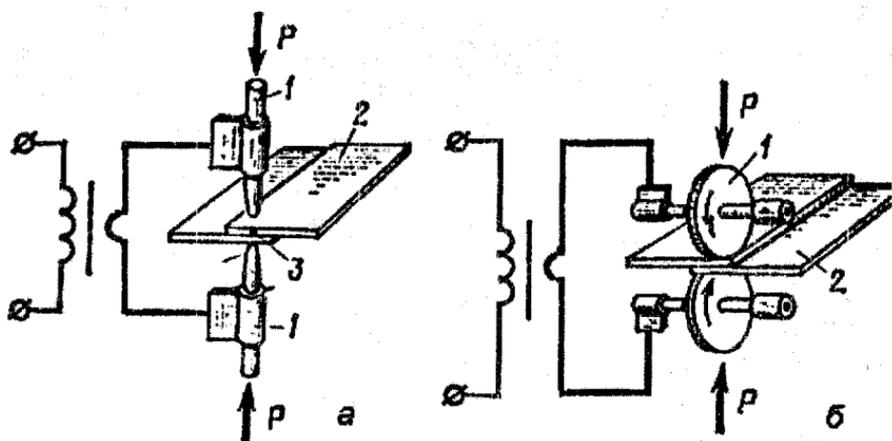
Принципові схеми точкового (а) і шовного контактного (б) зварювання
